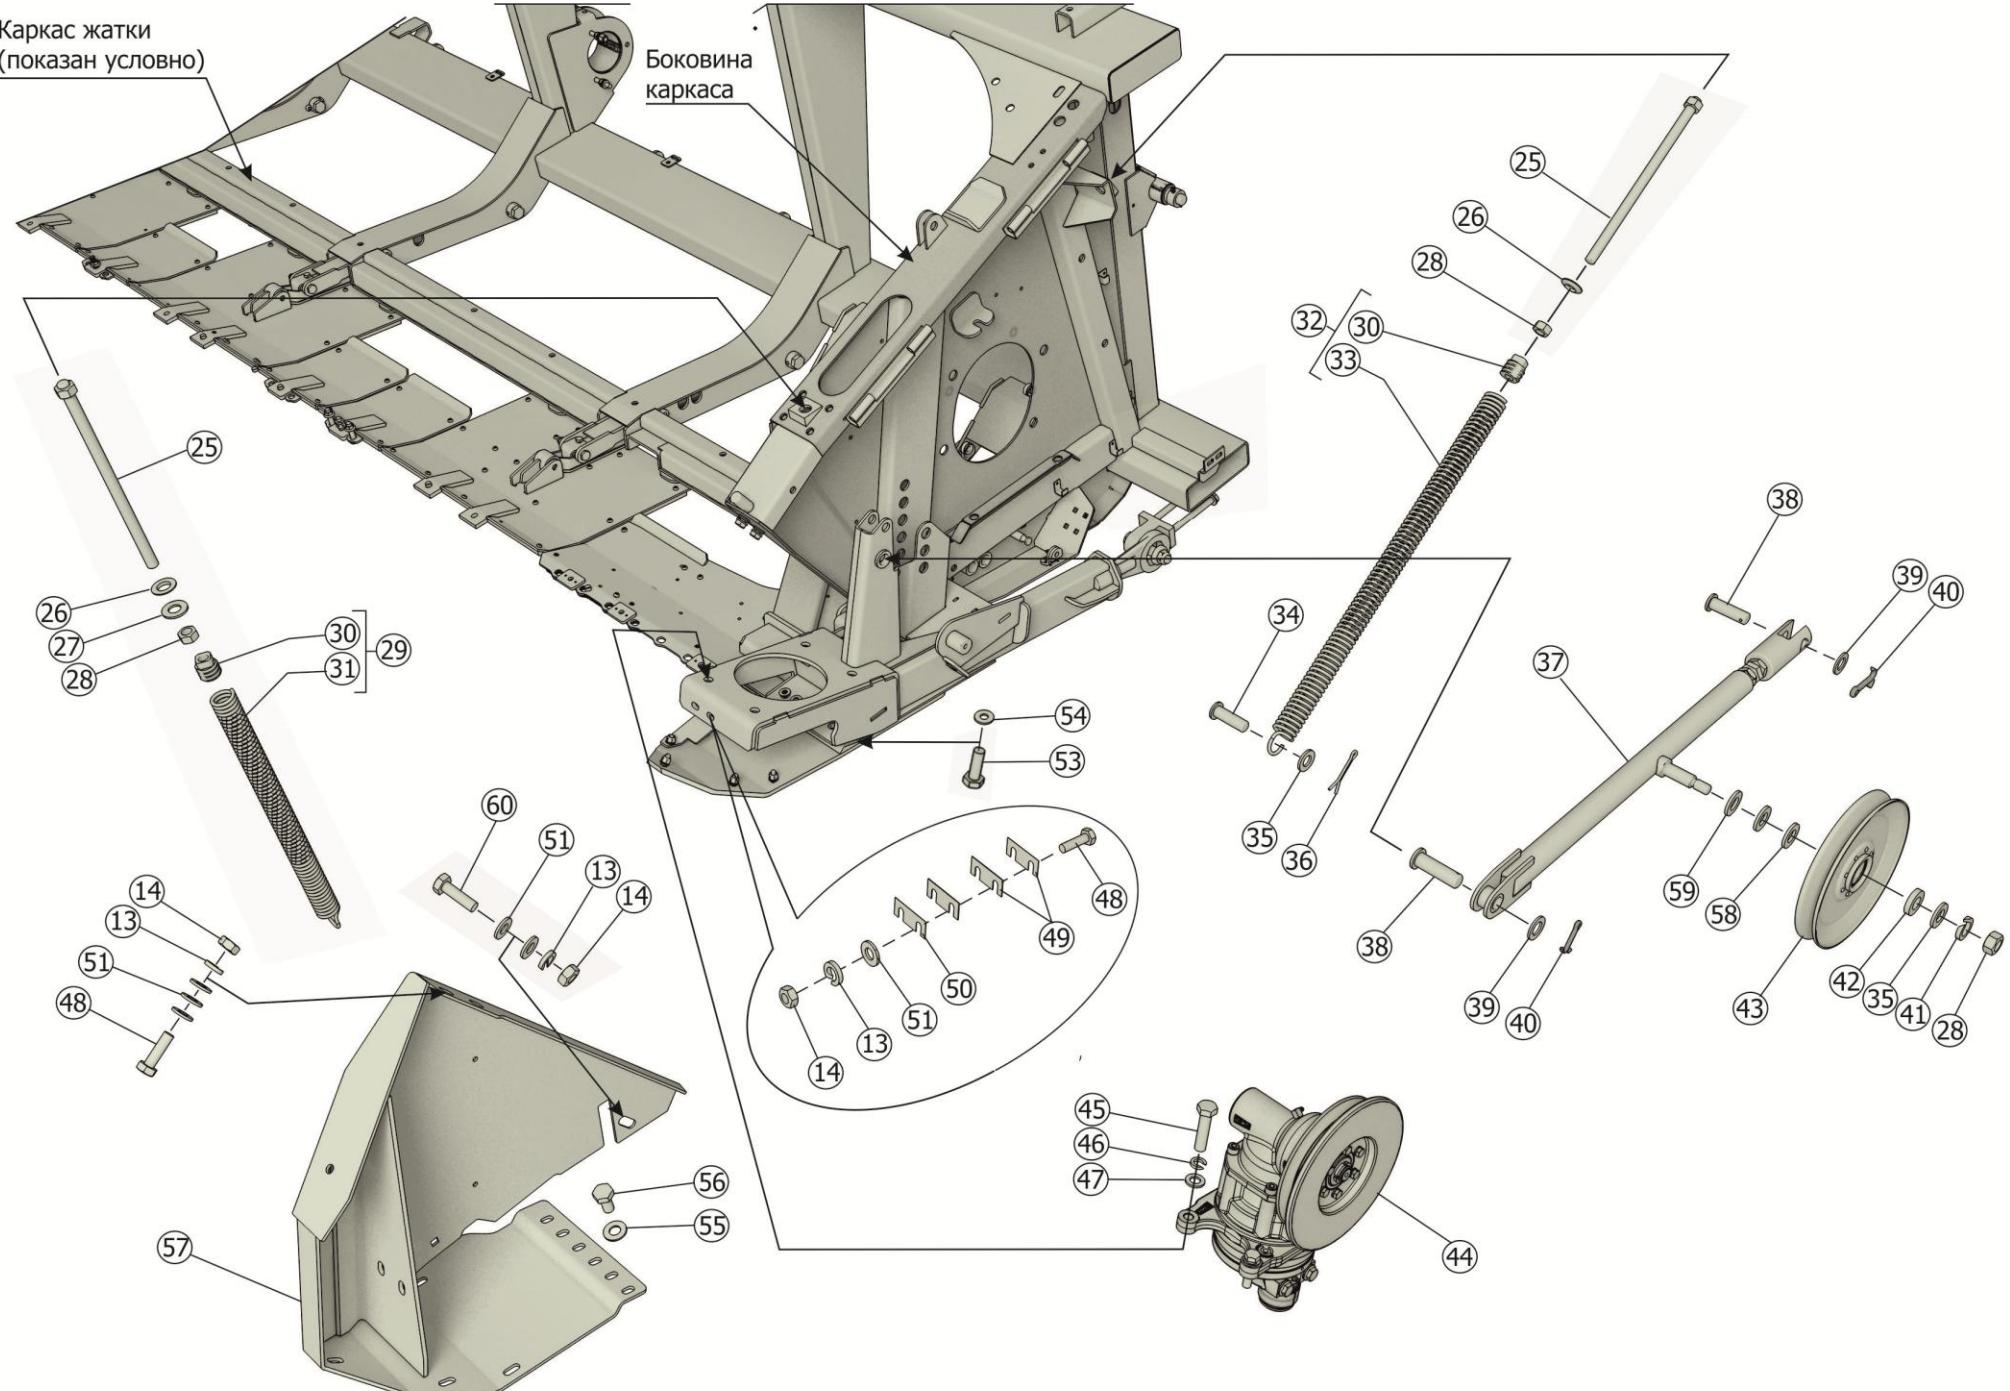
Привод режущего аппарата ЖСУ-901.01.03.500
